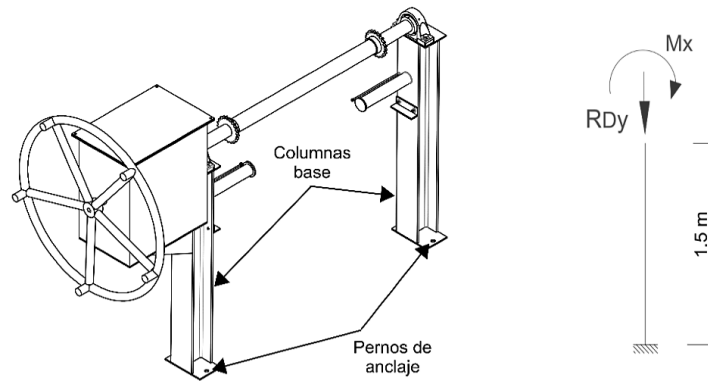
Columnas de base para mecanismo propuesto. Elaborado por: Galo Guañuna & Junior Ortiz
